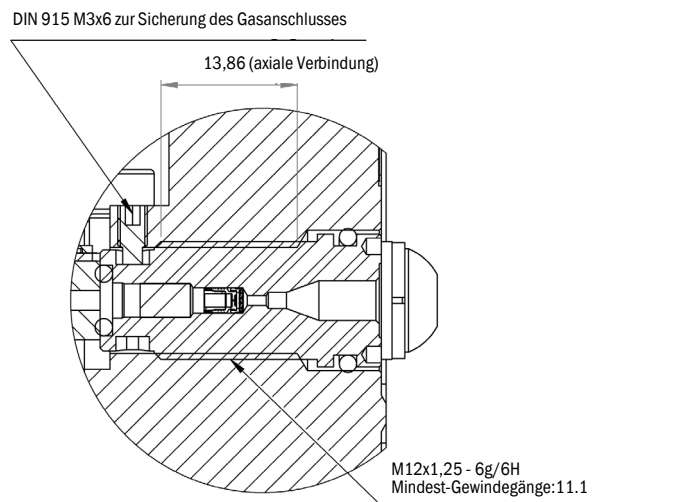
Verschraubter Flammweg zwischen Ex-Gasanschlüssen und Ex-Gehäusekörper
